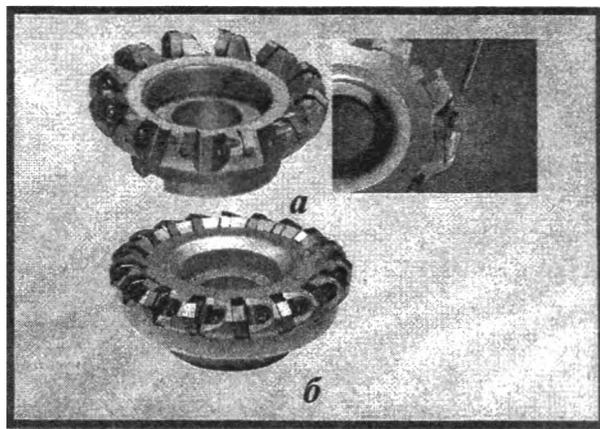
Конструкция фрез ISCAR с мелким шагом
